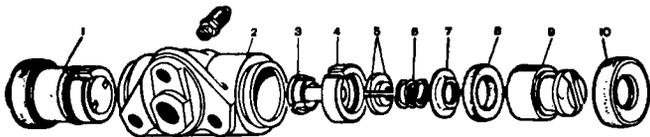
Детали колесного цилиндра: 1 - поршень в сборе; 2 - корпус цилиндра; 3 - упорный винт; 4 - упорное кольцо; 5 - сухари; 6 - пружина; 7 - опорная чашка; 8 - уплотнитель; 9 - поршень; 10 - защитный колпачок
